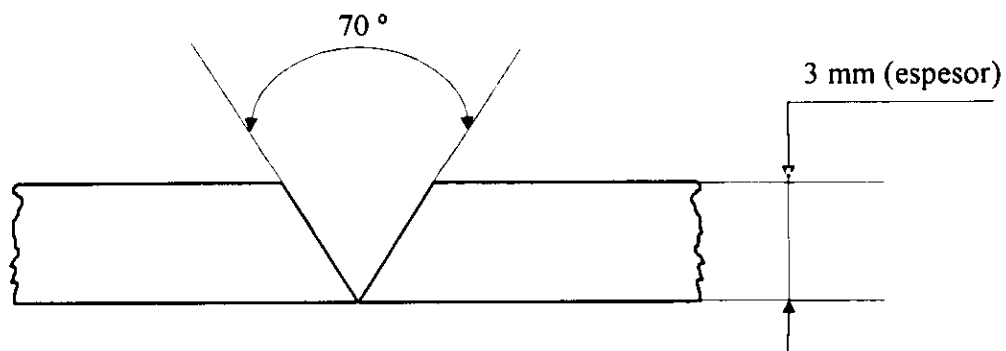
Junta tipo " V " sin talón, sin separación entre planchas. Muestras usadas para las soldaduras con dos pasadas de material de aporte.
